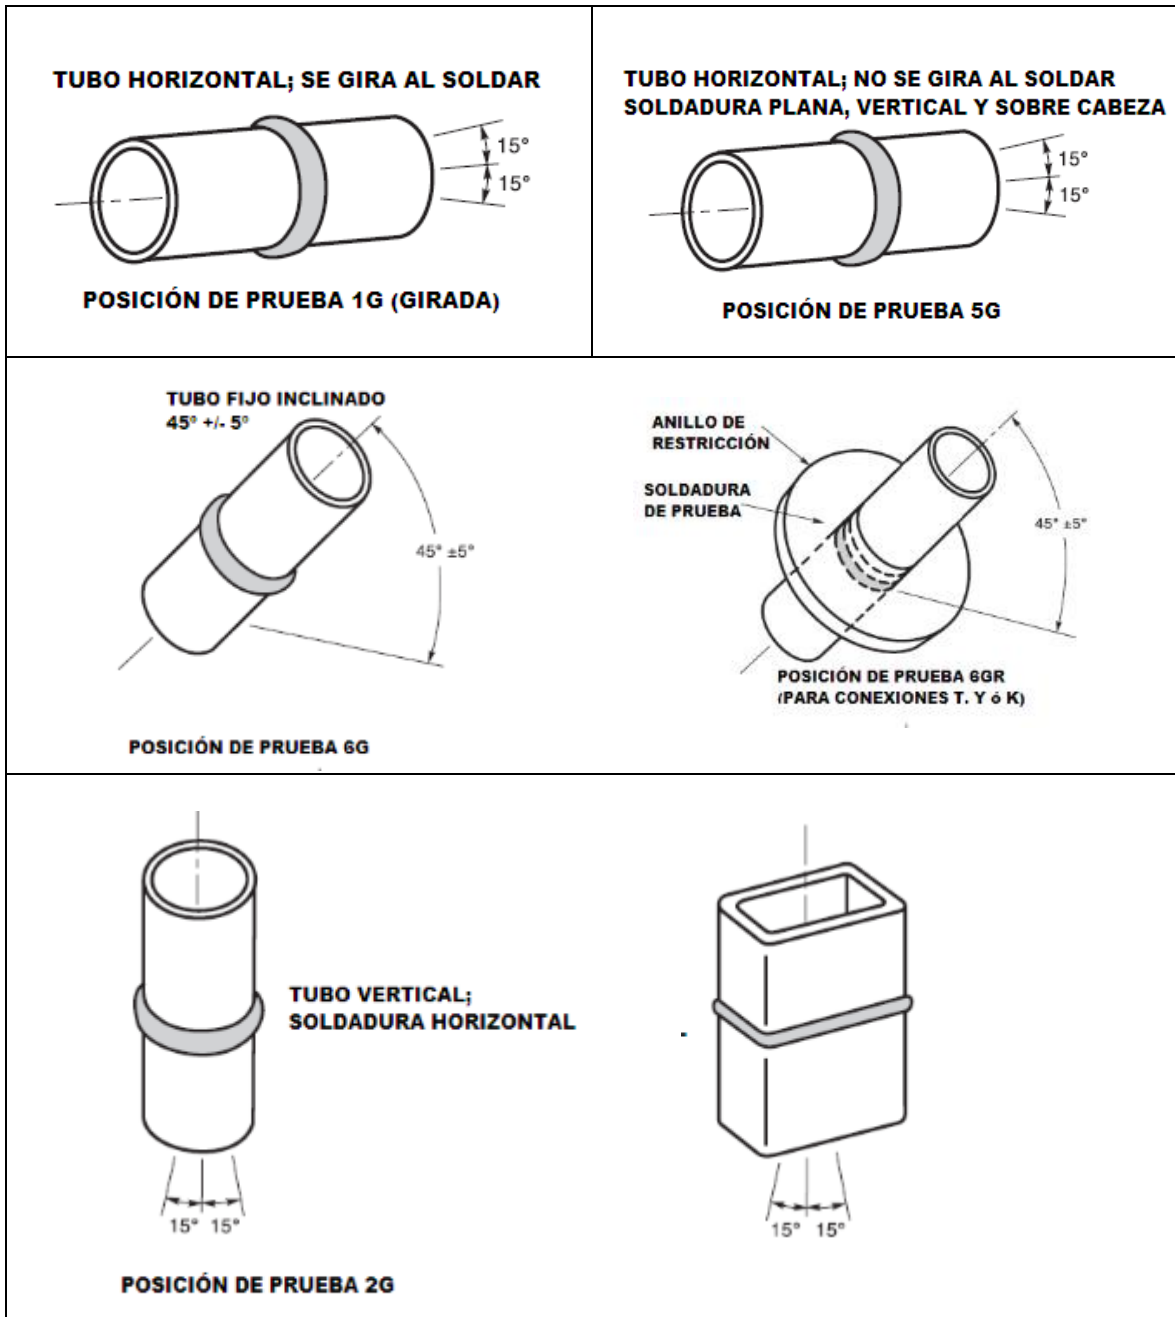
Posiciones de cordón de soldadura en ranura de tubos
